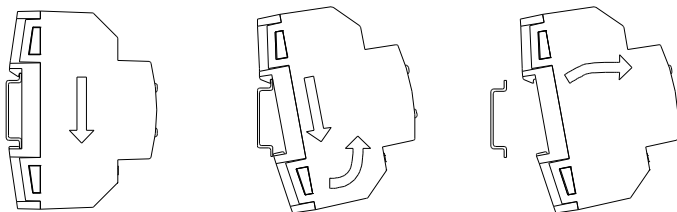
Montaje de FANinBOX 110V 1CH en carril DIN
